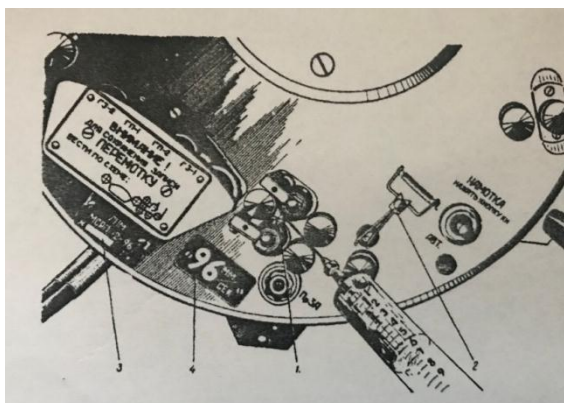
Мاستило верхнього підшипника тонвала. 1 – провідний вал; 2 – контактний пристрій автостопу; 3 – шильдик; 4 – шильдик з написом.
